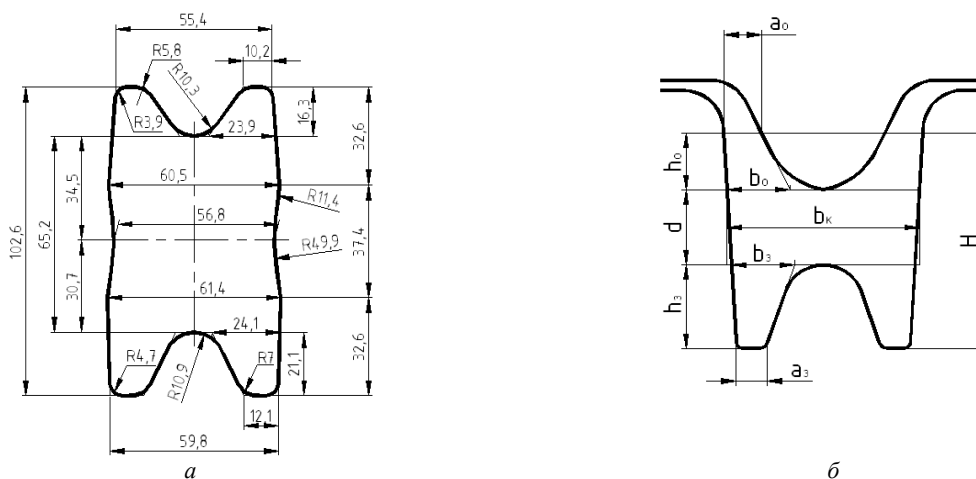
Поперечное сечение исходной заготовки (а) и черновой закрытый балочный калибр (б)
